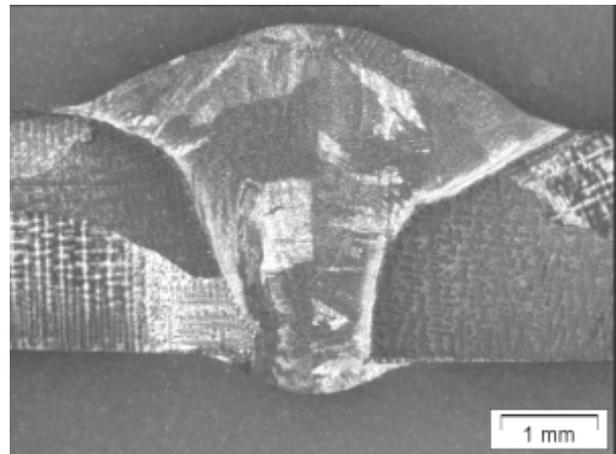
MSG-Schweißnaht (CMT) an einem hitzebeständigen Werkstoff
